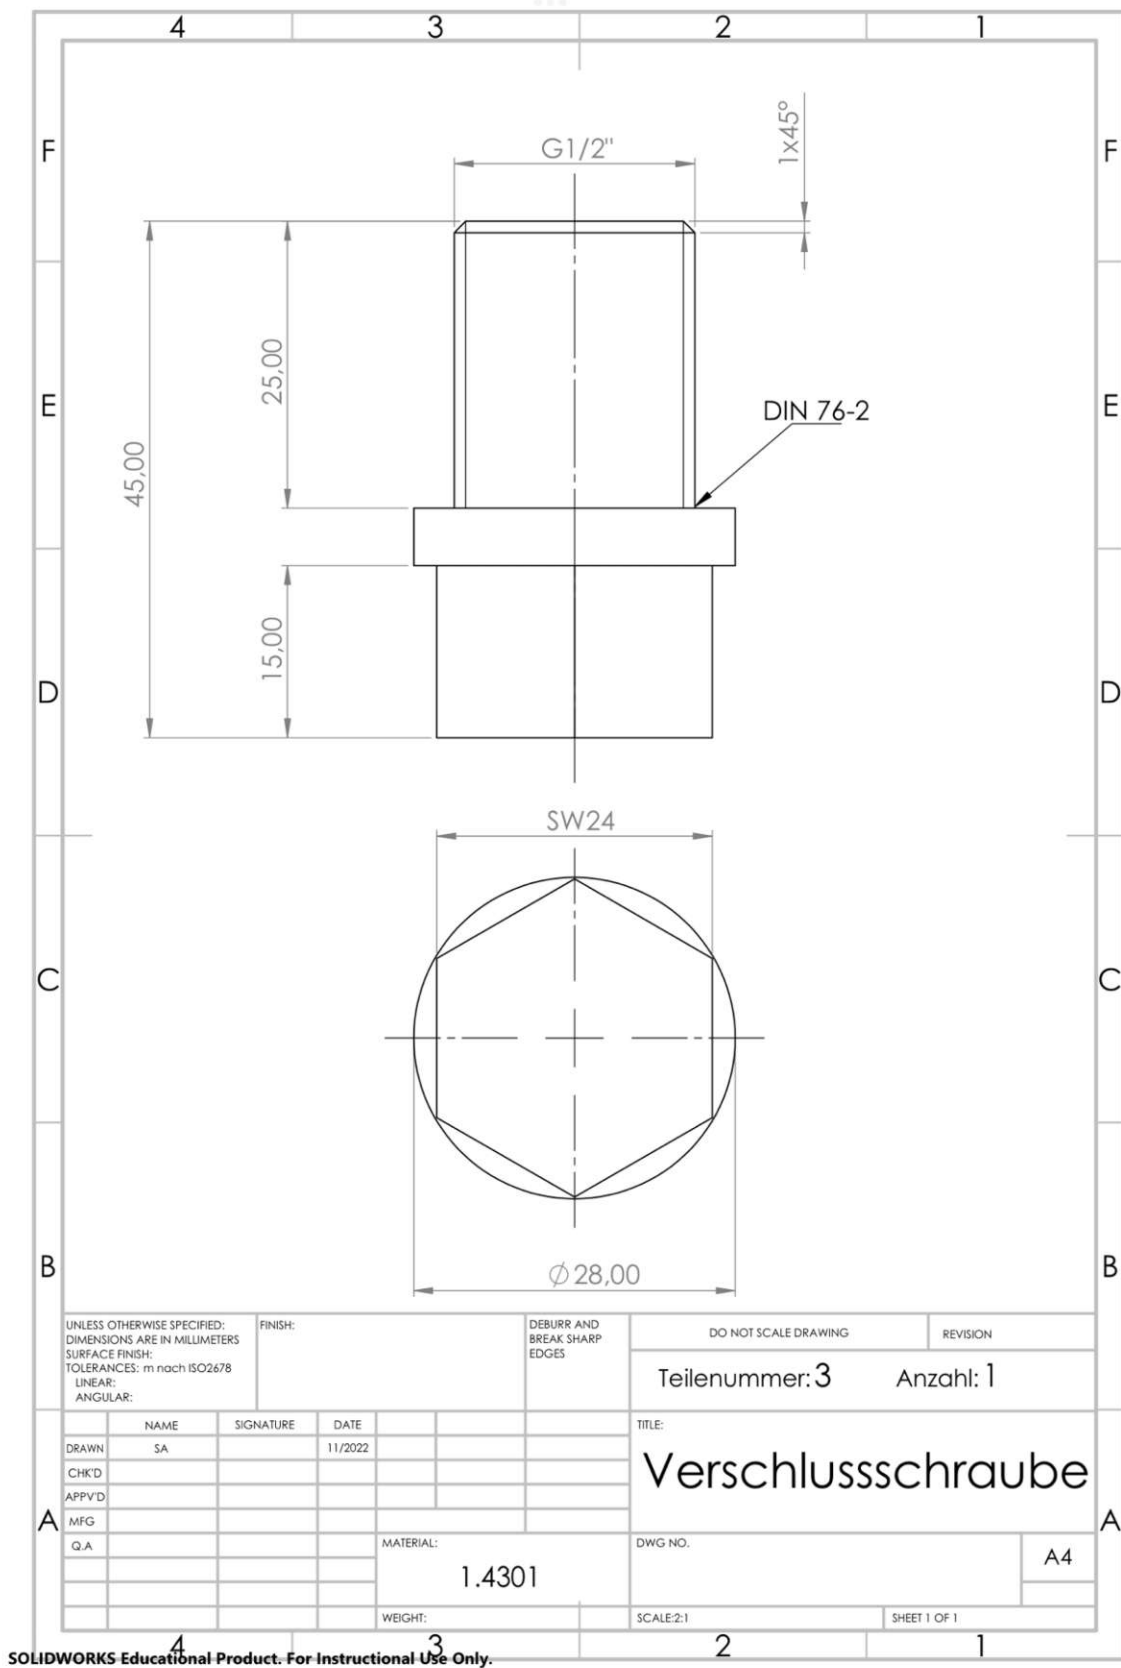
Technische Zeichnung der Verschlusschraube (Teilenummer 3)
